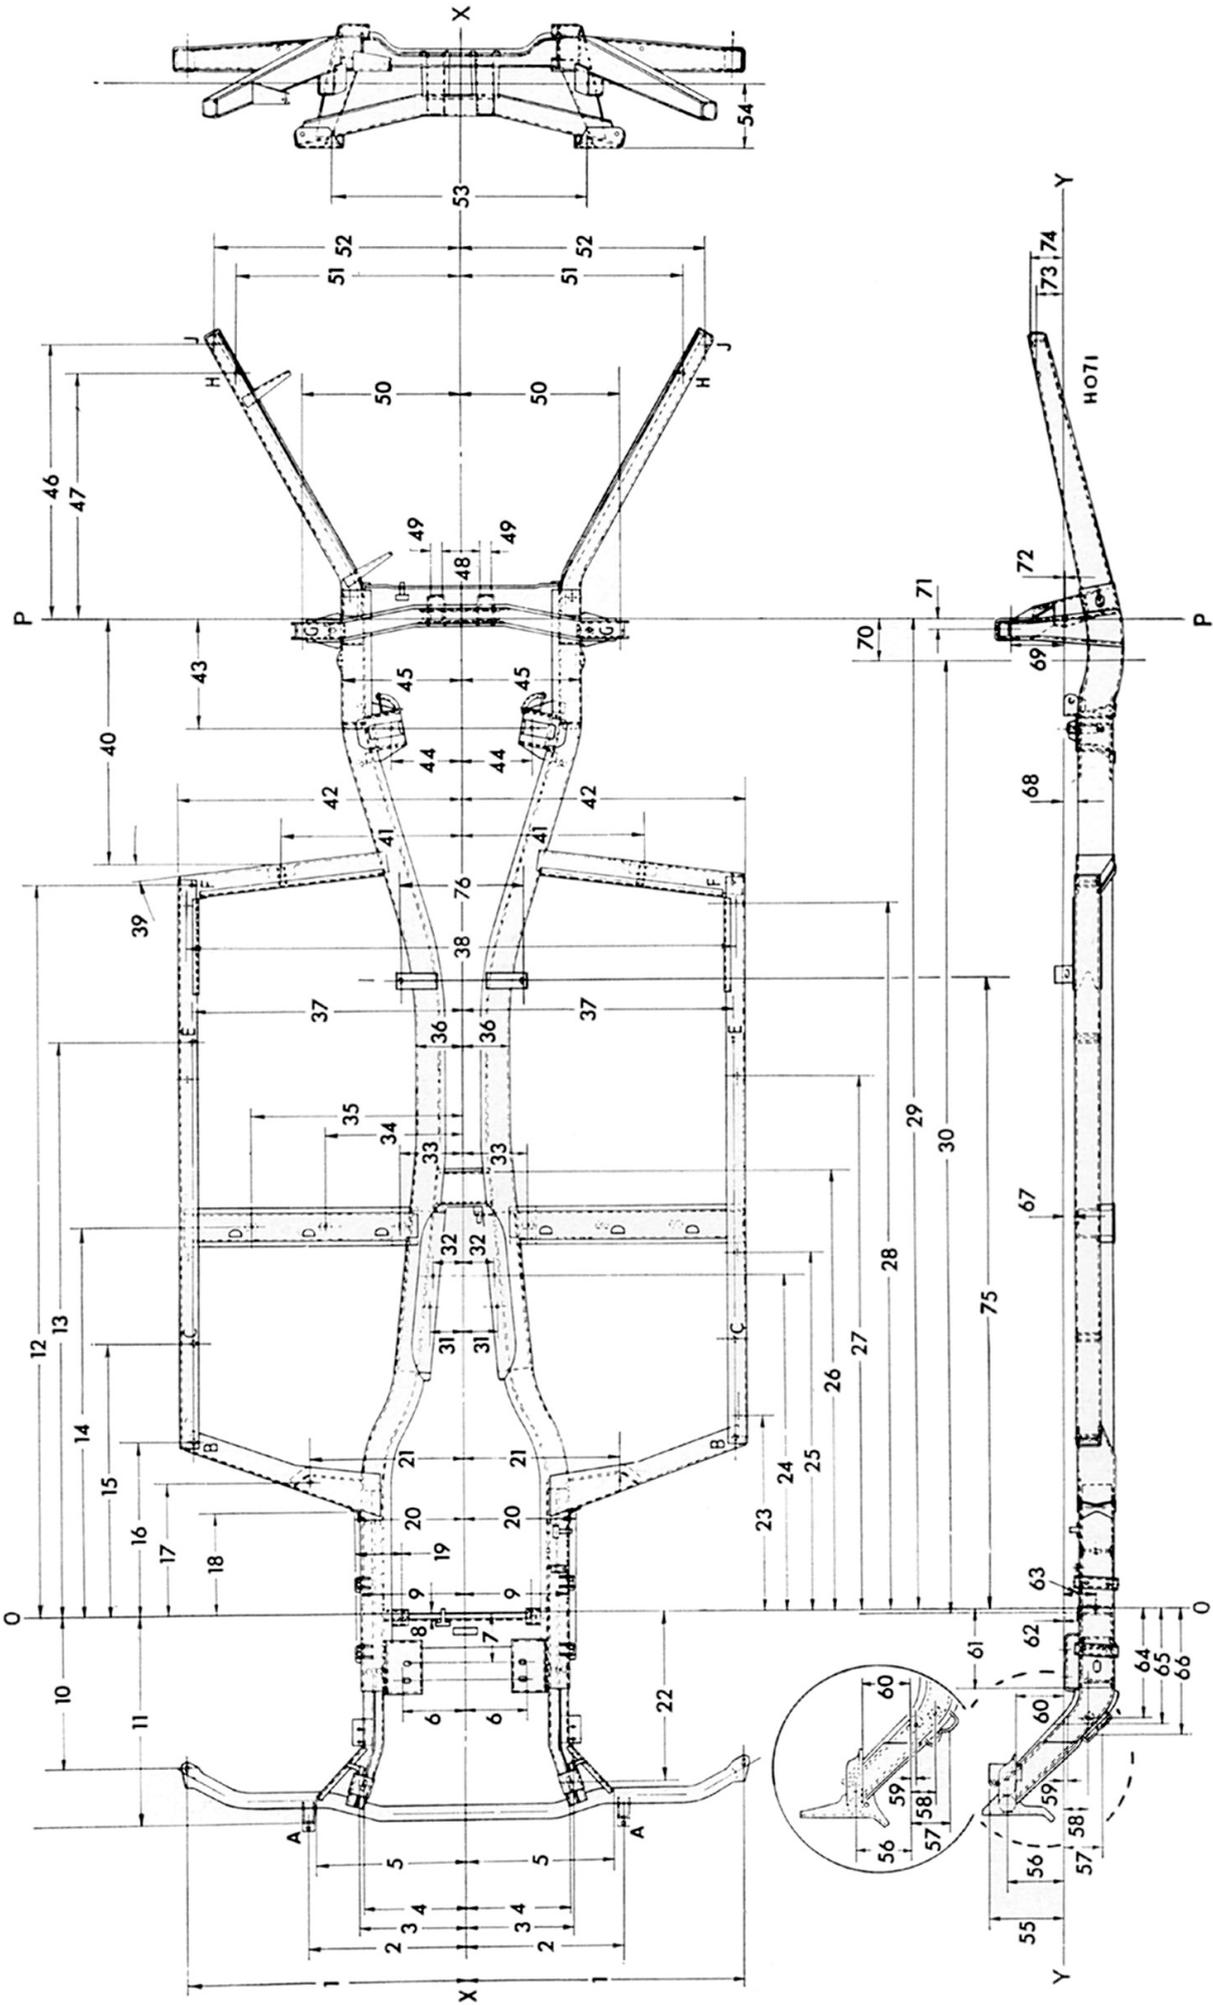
Châssis - Herald 1200, 12/50, 13/60 et Vitese 1600 (Herald 1200 and 12/50 : détails en encadré).
